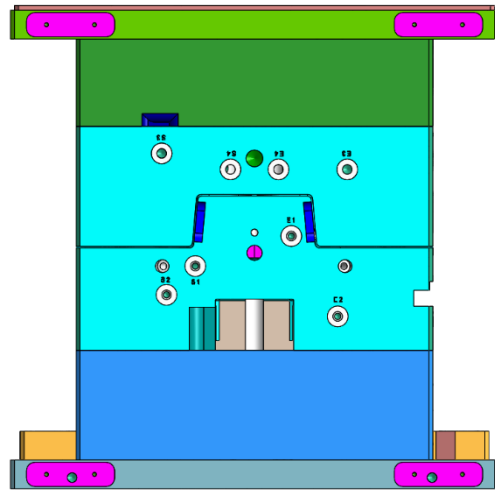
Estrutura, vista do lado das entradas e saídas da refrigeração
